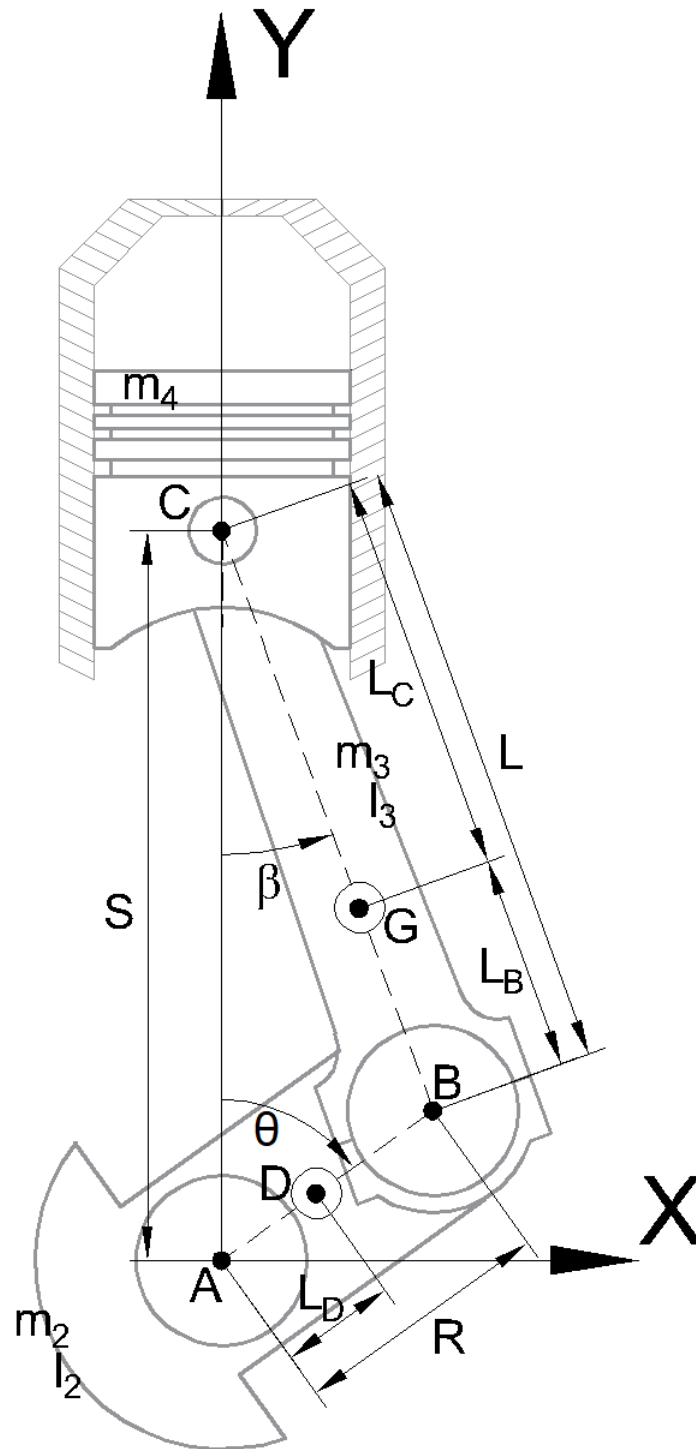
Dimensiones principales en el mecanismo pistón-biela-manivela [9]
